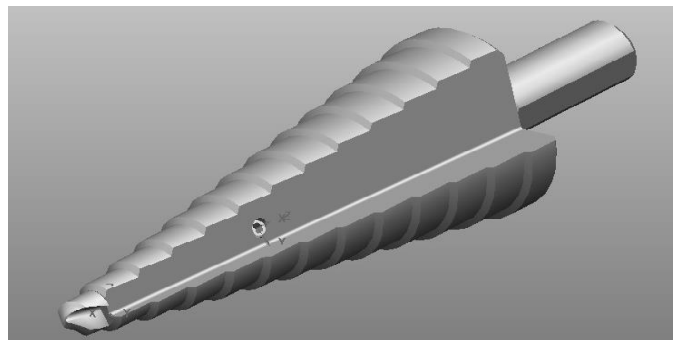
3D модель інструменту "Конічне свердло"
